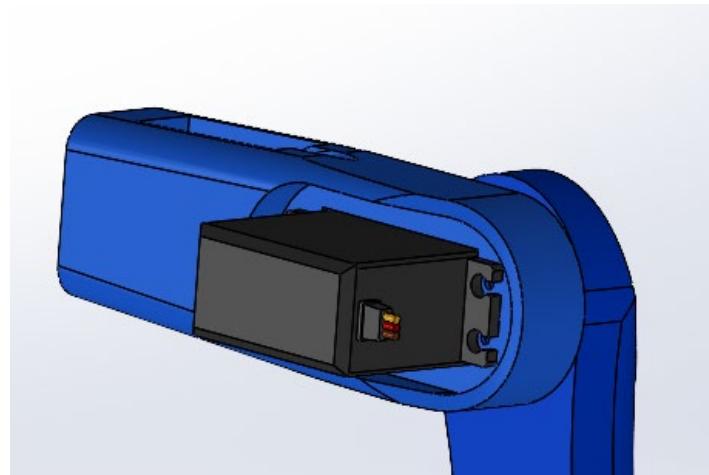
Servo Motorlar ile Robot Gövdesi Montajı
